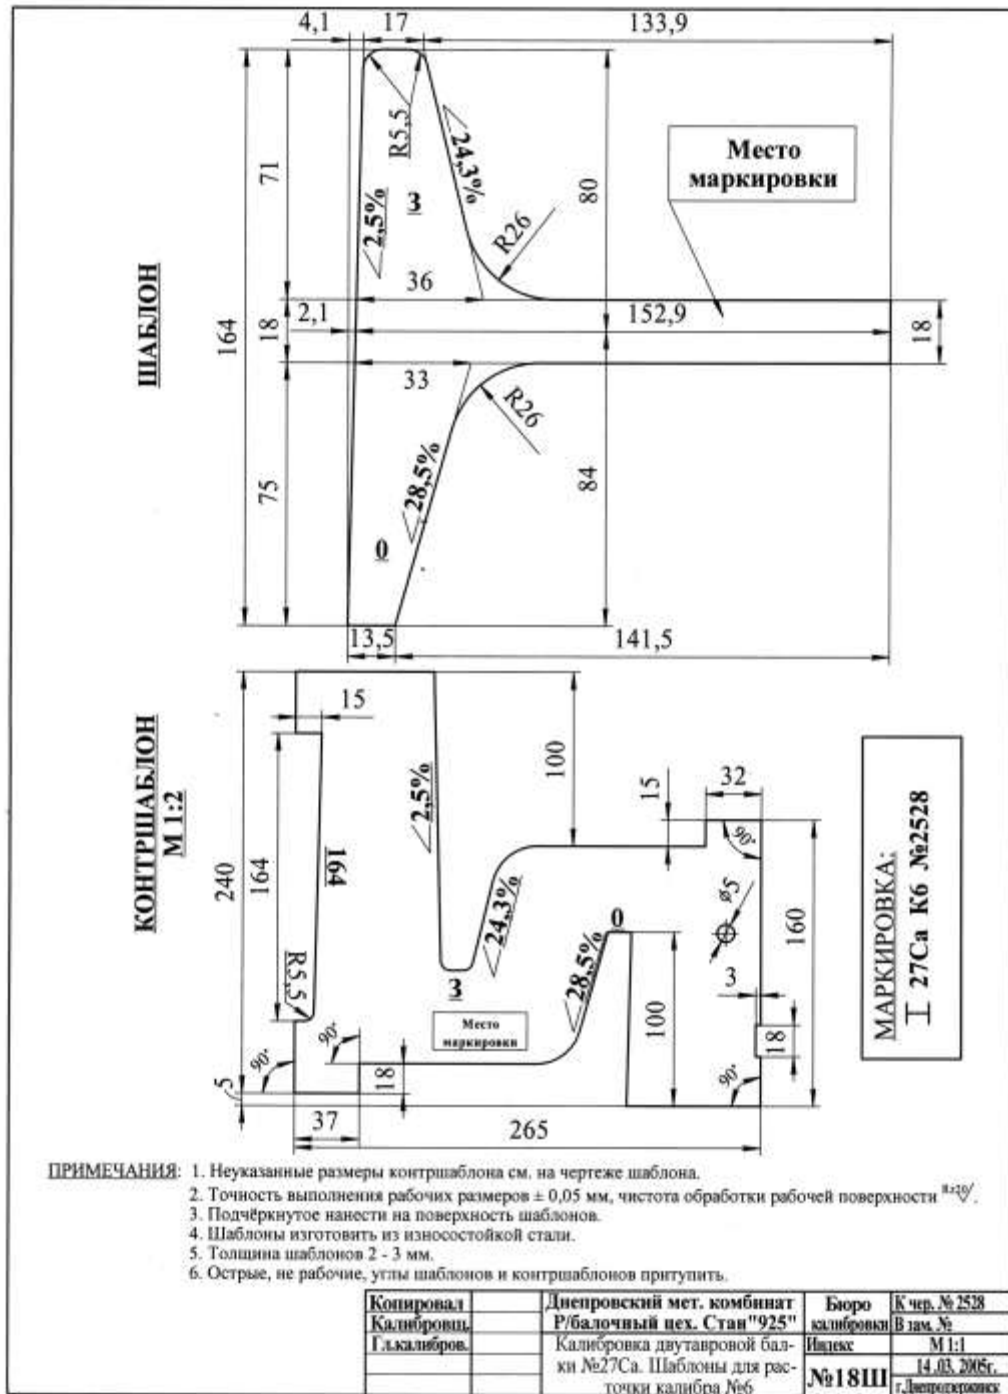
Креслення шаблону та контршаблону для розточування калібру № 6 для прокатування двотаврової балки №27Са
